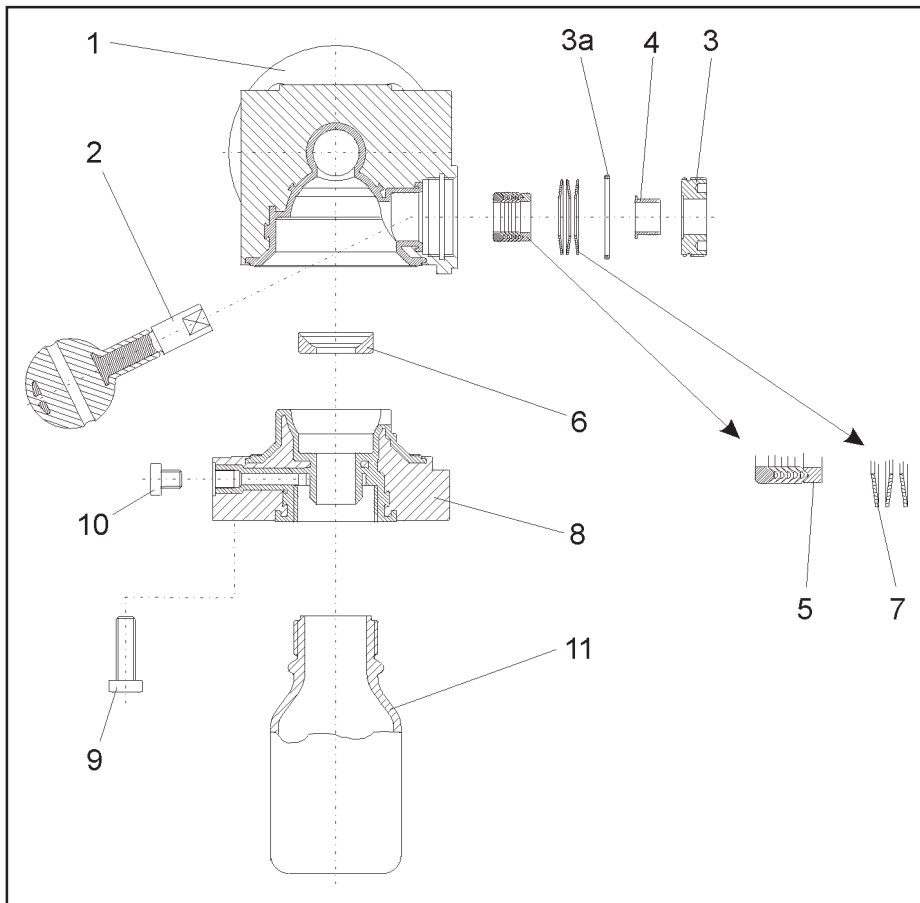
Explosionszeichnung des Probenehmerhahns BR 27e
